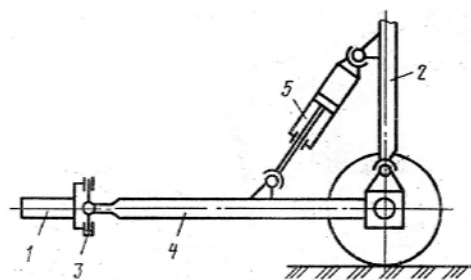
Схема тягово-сцепного догружающего устройства скрепера
